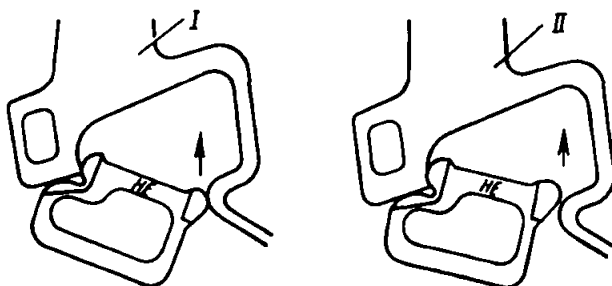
Проверка ширины зева корпуса автосцепки шаблоном 821р-1:
